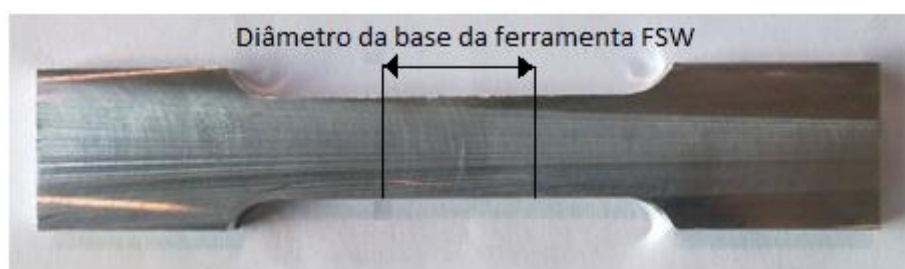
Provete de tração obtido após maquinação das chapas soldadas
